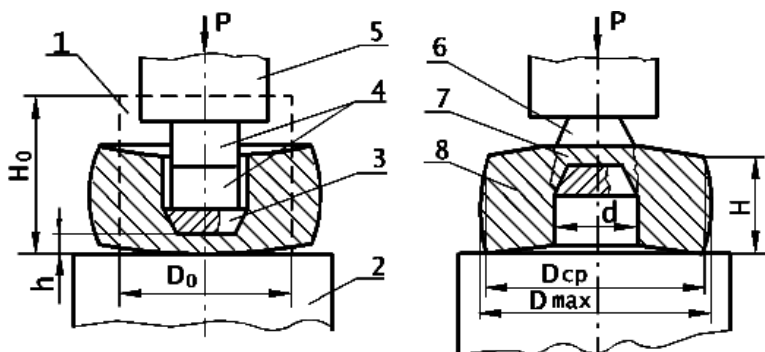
Схема прошивки сплошным прошивнем: 1 – заготовка; 2, 5 – бойки; 3 – прошивень; 4 – надставка; 6 – прошивень просечной; 7 – выдра; 8 – прошитая поковка
